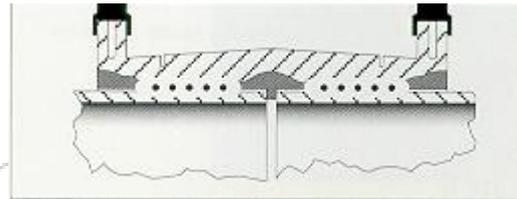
Solda executada. O indicador de solda preenchido com Polietileno
